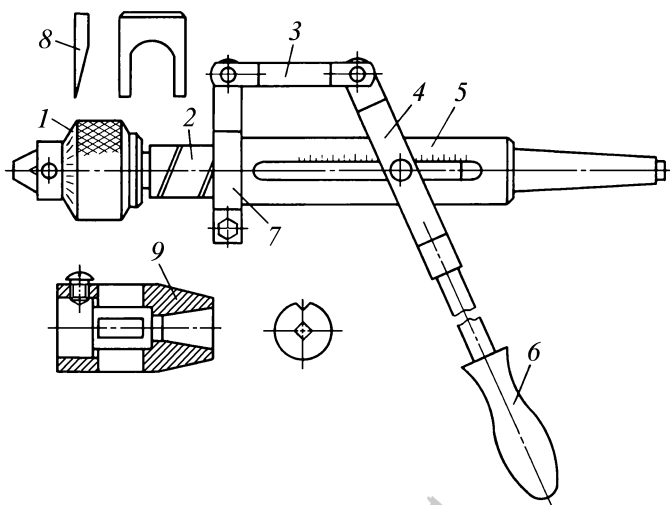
Приспособление для сверления глубоких отверстий и нарезания резьбы
